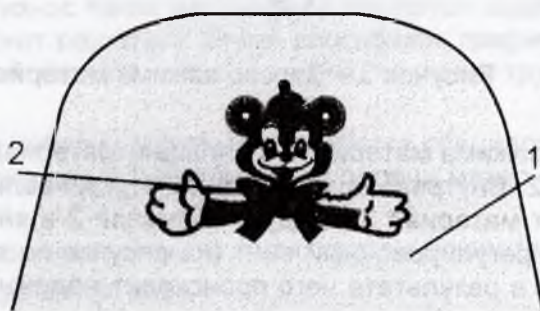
Деталь галантерейного изделия с вышивкой
